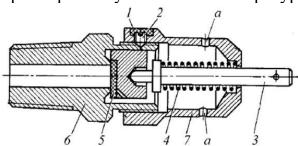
Предохранительный клапан: а -отверстия для выхода газа в атмосферу; 1-шайба; 2-стопорный винт; 3 - шток; 4 - пружина; 5 - клапан;
